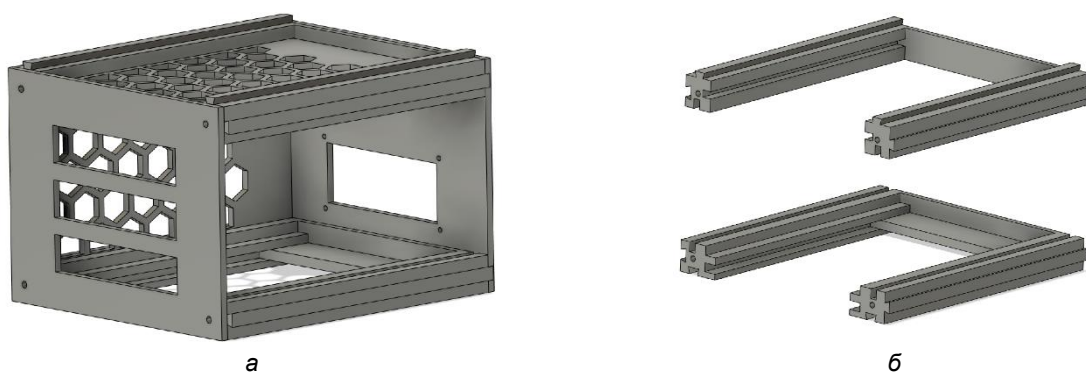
3D-модель: *а* – унифицированный корпус; *б* – основа корпуса
